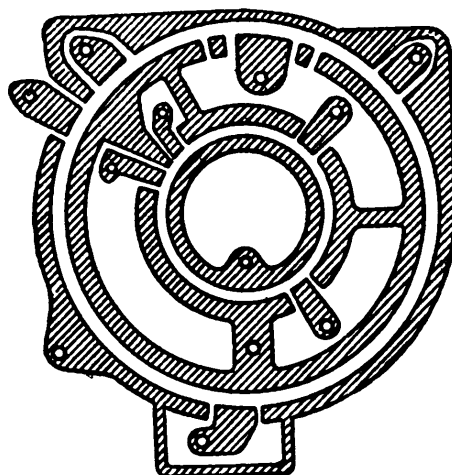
Контакты сложного переключателя, изготовленные печатным способом
